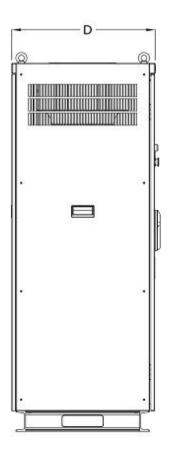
Габаритные размеры PD310-A4 (630~710 кВт) (металлический корпус)
